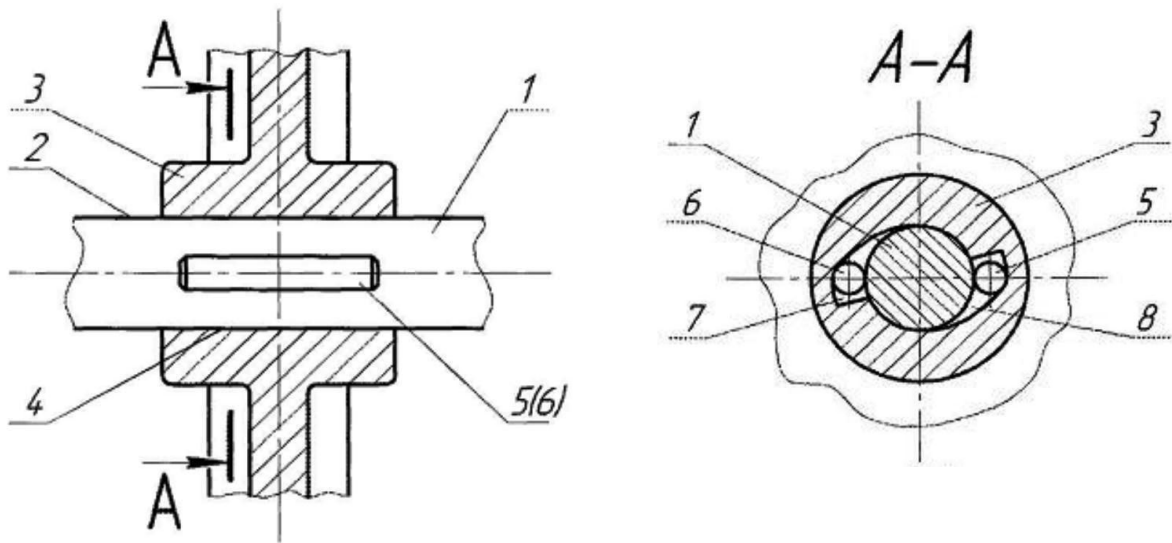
З'єднання деталі з валом (запропонована конструкція):
